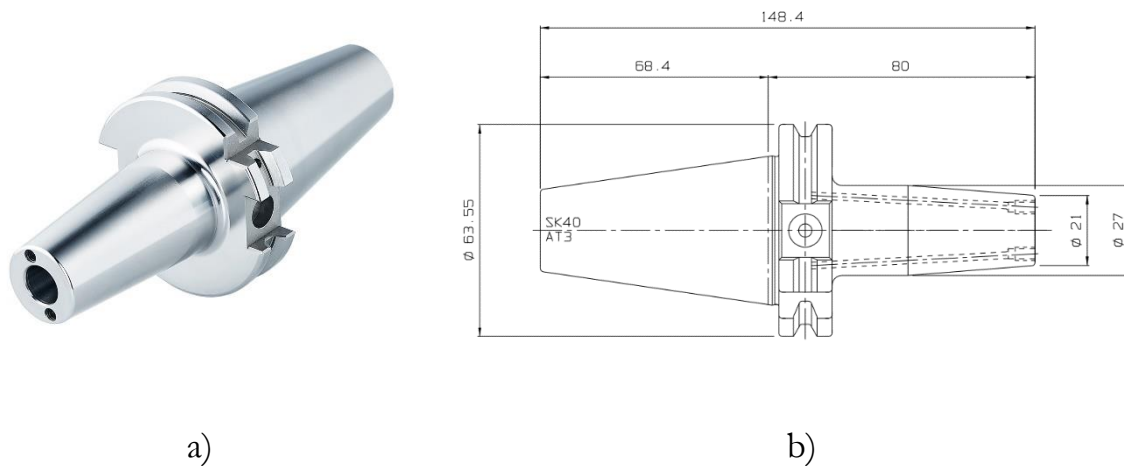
Sistema de fixação: a) cone térmico; b) desenho técnico do cone térmico (Kemmler, 2023).
